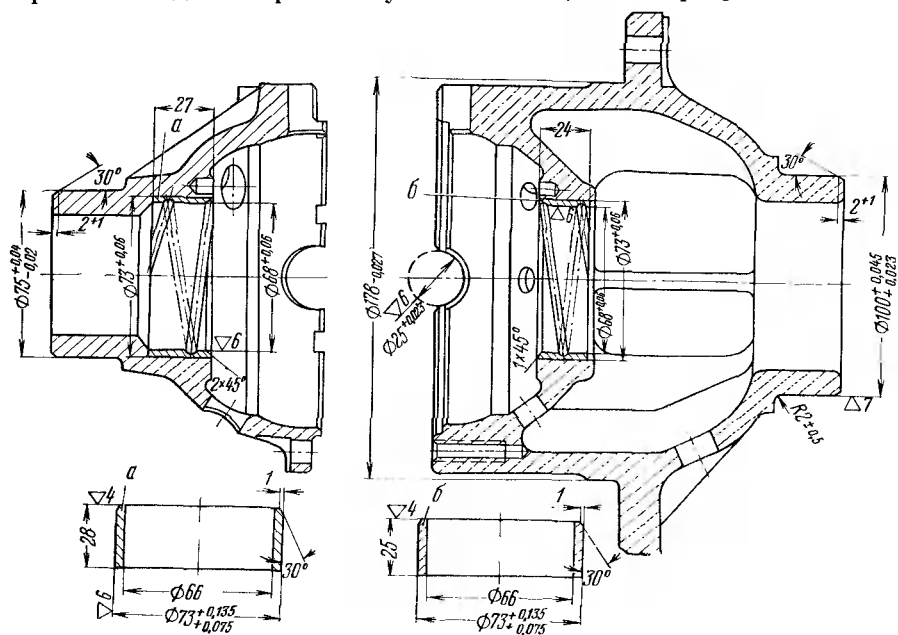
Ремонтные втулки чашек коробки дифференциала под цапфы полуосевых шестерен:
